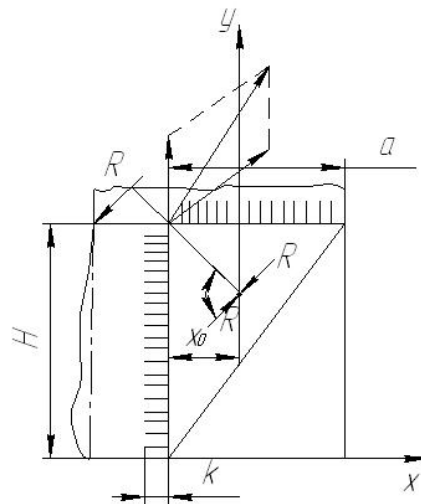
Схема дії сил при зварному з'єднанні.
